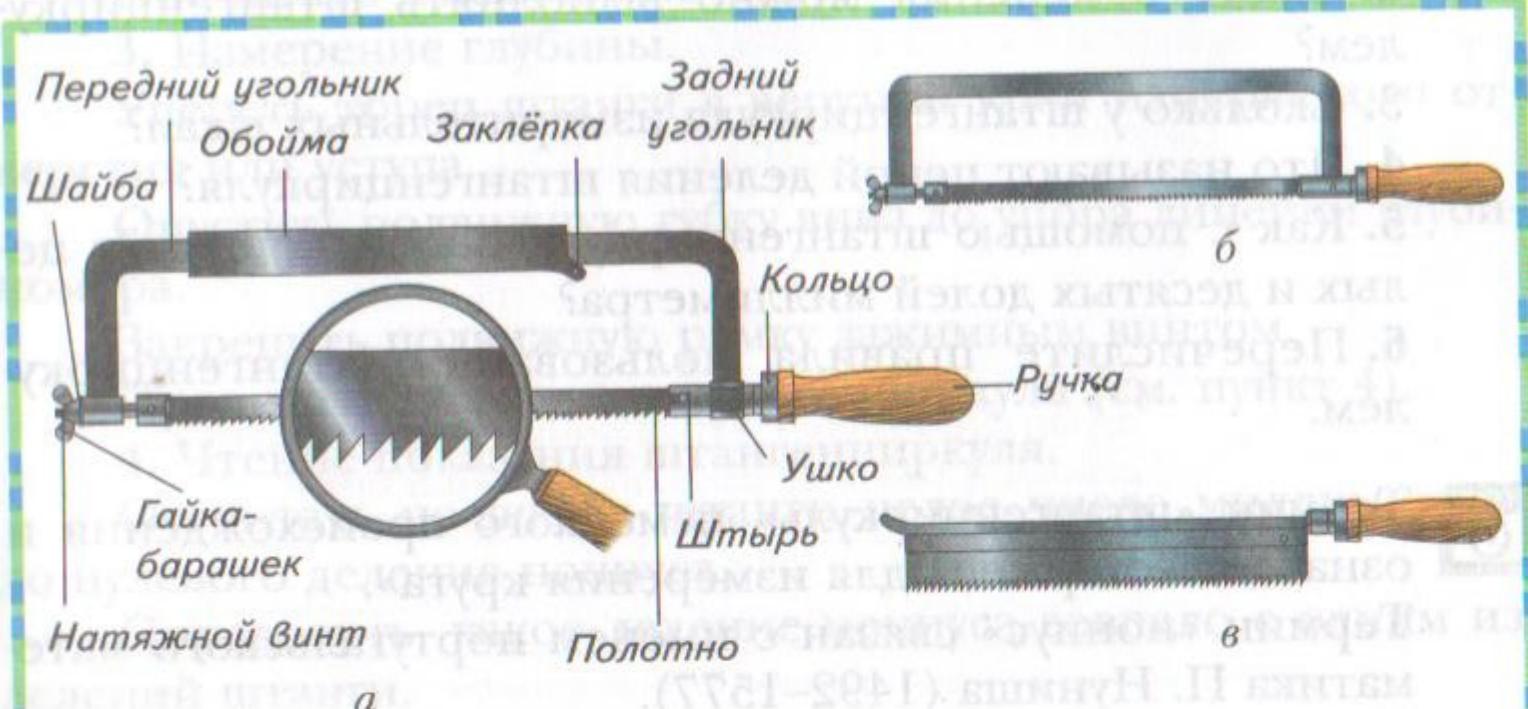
Виды ножовок: а – ножовка с раздвижной рамкой и её устройство; б – ножовка с цельной рамкой; в – ножовка-шлифовка
